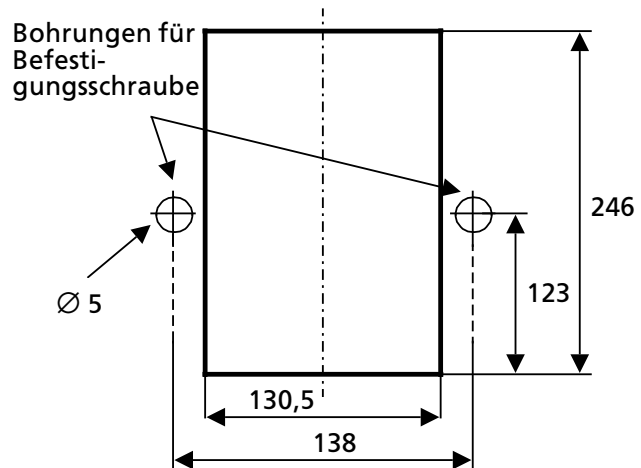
Ausschnittmaße (in mm) für Schalttafeleinbau
